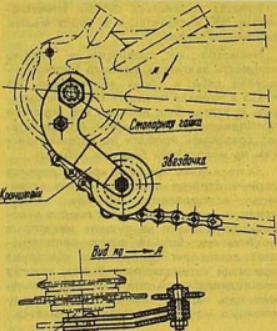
Устройство для регулировки натяжной цепи ножного привода.
